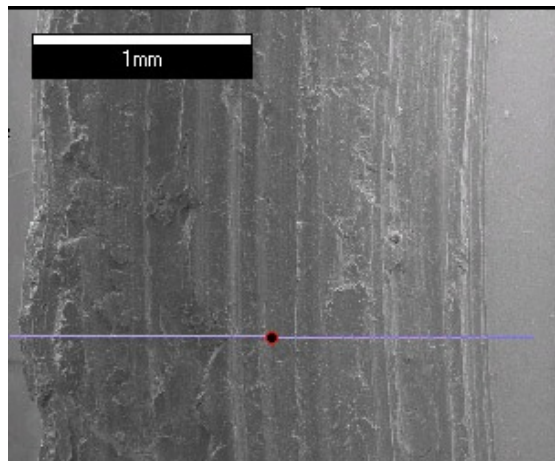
Detaillierte Ansicht auf die Oberfläche einer Gewindeflanke
